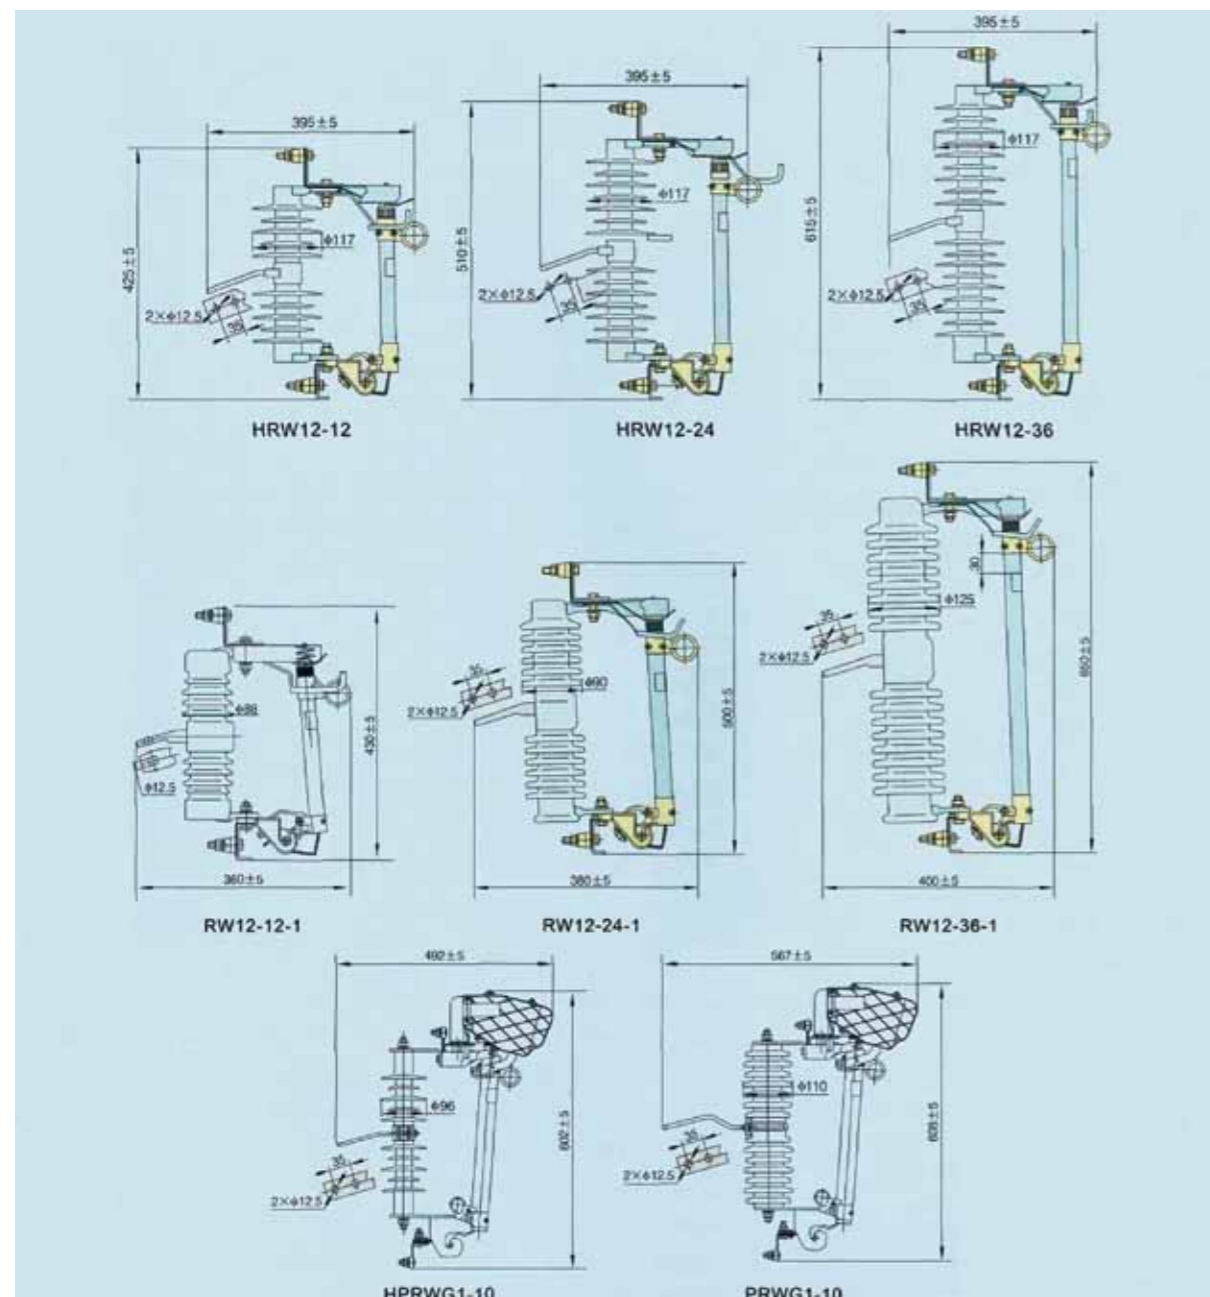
Внешний вид и размеры откидывающегося плавкого предохранителя
